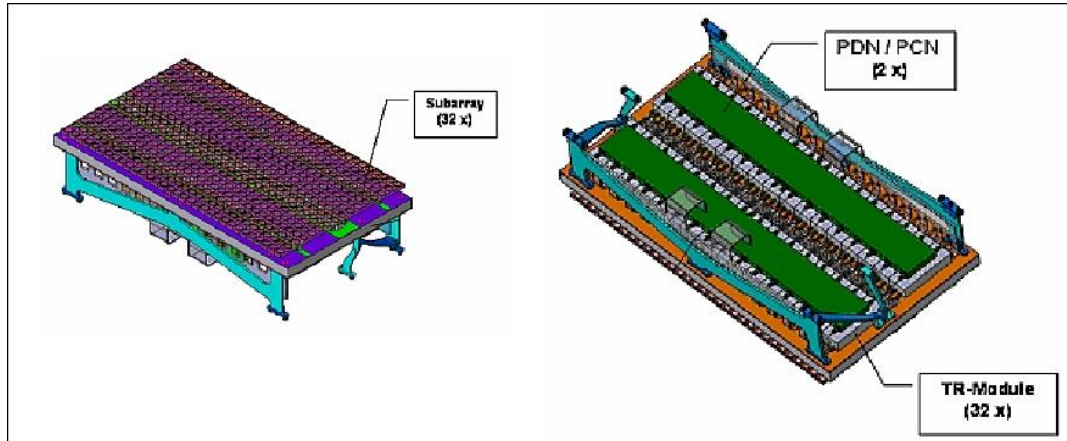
Vistas array X-SAR (Imagen de ESA CASA Espacio)
